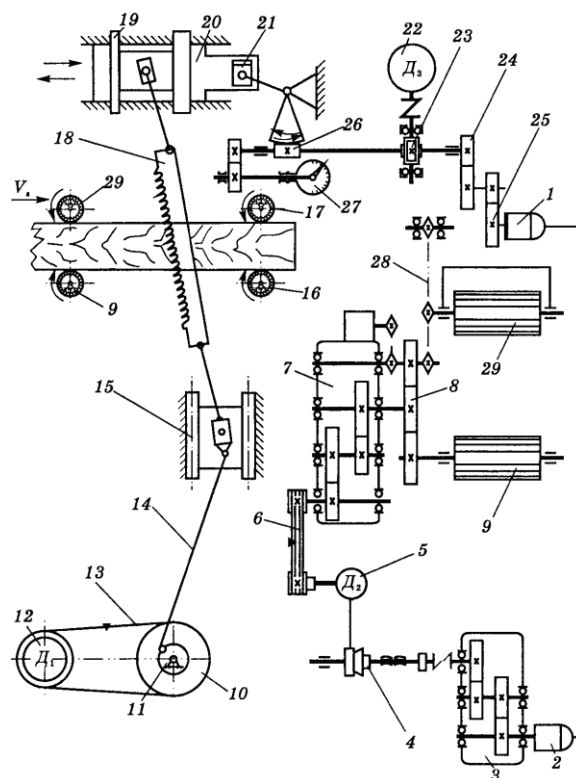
Кінематична схема двоповерхової лісопильної рами з безперервною подачею і регульованим нахилом пилки: 1 – ведучий сельсин; 2 – ведений сельсин; 3, 7 – редуктор; 4 – реостат; 5 – електродвигун механізму подачі; 6, 13 – клинопасова передача; 8, 24, 25 – шестерні; 9 – нижні вальці; 10 – шків, 11 – колінчастий вал; 12 – електродвигун механізму різання; 14 – шатун; 15 – нижні напрямні; 16, 17 – вальці; 18 – пилкова рамка; 19 – напрямні; 20 – плита; 21 – кулісний механізм; 22 – електродвигун; 23, 26 – черв'ячна передача; 27 – показчик; 28 – ланцюгова передача; 29 – верхні вальці
